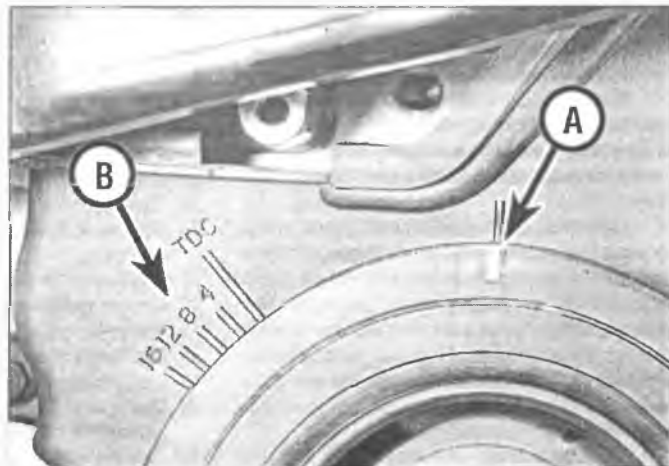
,б. Совместите выемку на шкиве коленчатого вала с указателем (А) на нижней крышке ремня газораспределительного механизма
